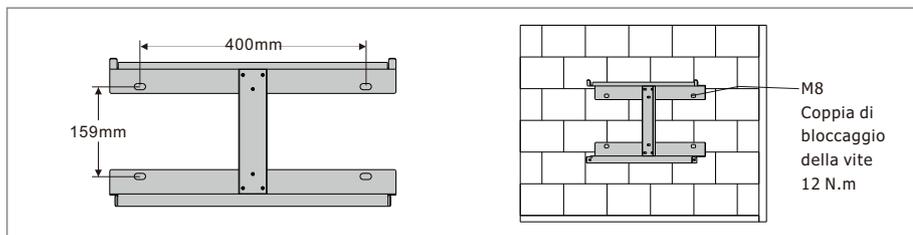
Installazione della piastra di sospensione dell'inverter
